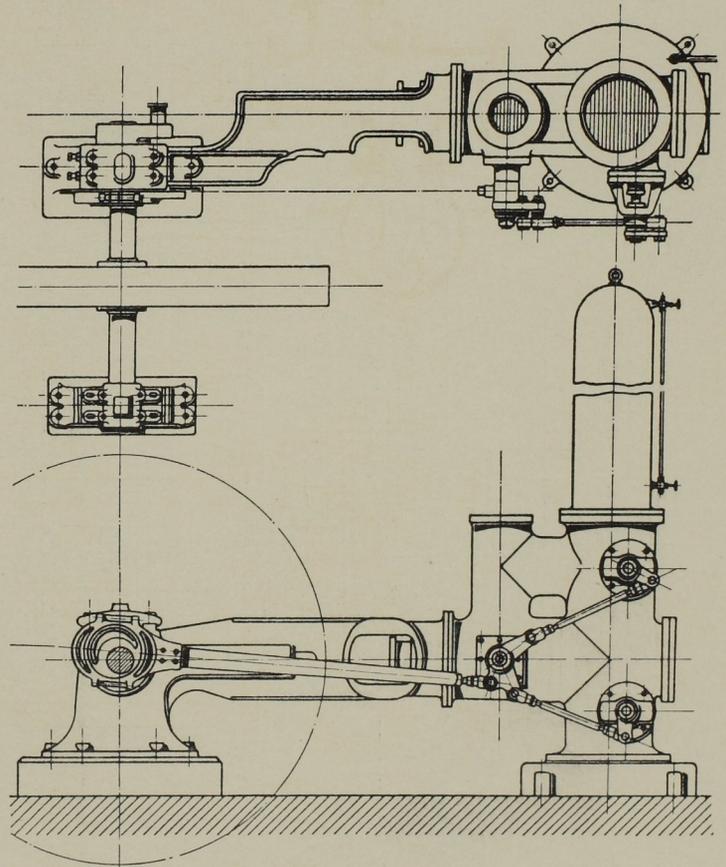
Seitenansicht und Grundriss der Pumpe.
